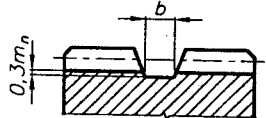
Размеры канавок для выхода червячных фрез
